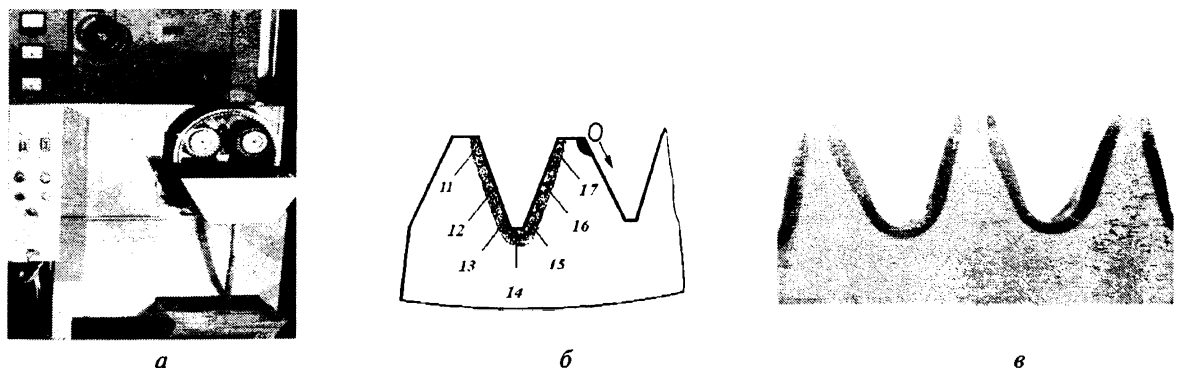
Индукционная установка для закалки внутренней зубчатой поверхности шестерен модулем 4,0 и 4,5 мм колесной передачи автомобилей Минского завода колесных тягачей (а), схема передвижения индуктора относительно зубчатой поверхности (б) и расположение зоны закалки в сечении зубчатой поверхности шестерен (в)
